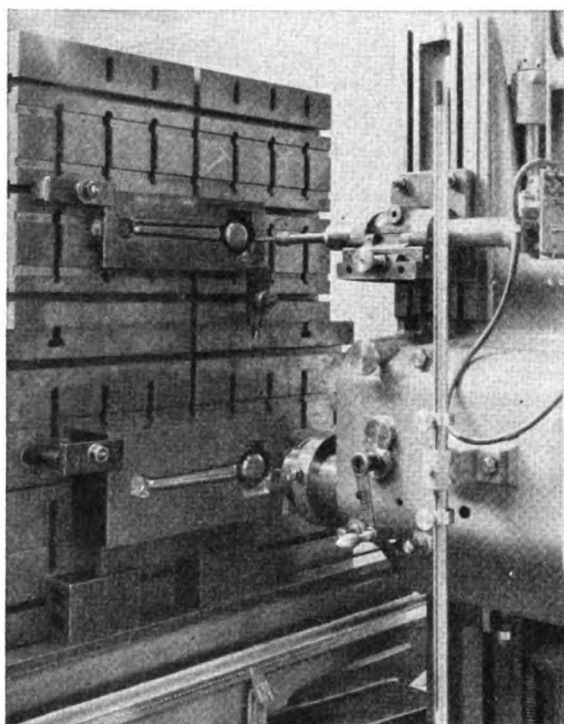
Modell mit Fühlhebel (oben) und Werkstück mit Fräser (unten) der Maschine nach Abb. 8a.
